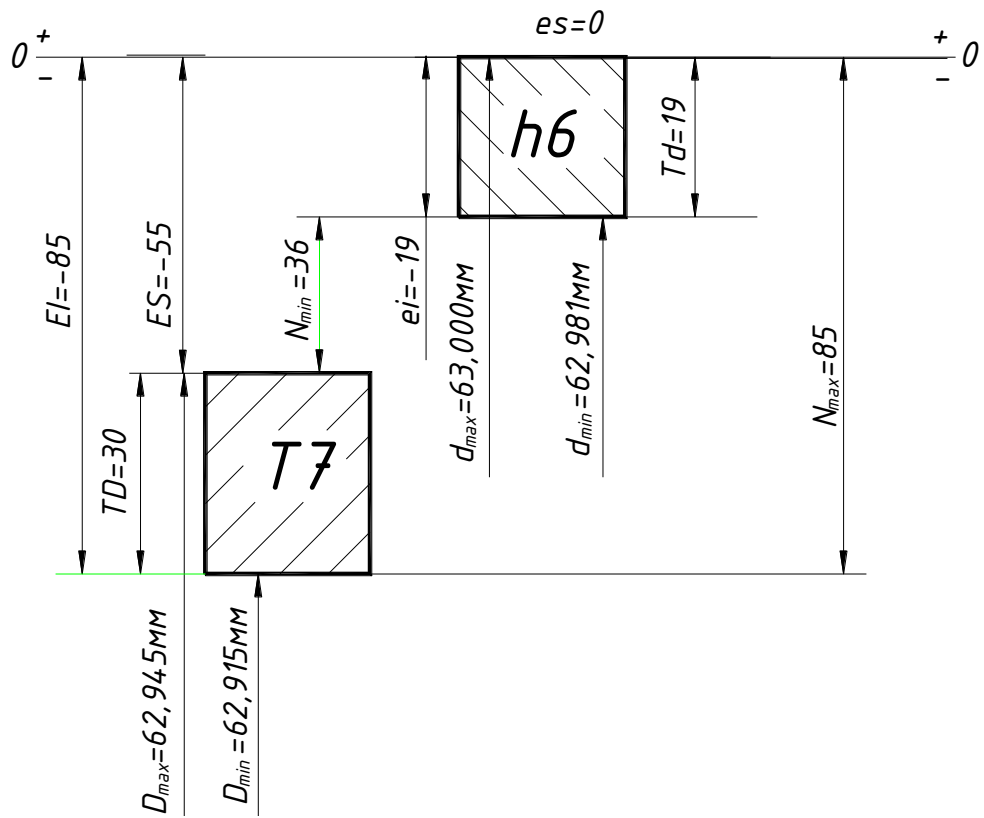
Схема розташування полів допусків отвору і вала
